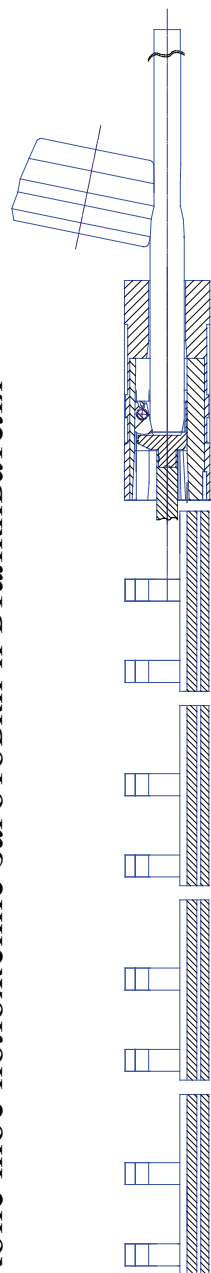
Схема процесса прокатки заготовки в трехвалковом обжимном стане
